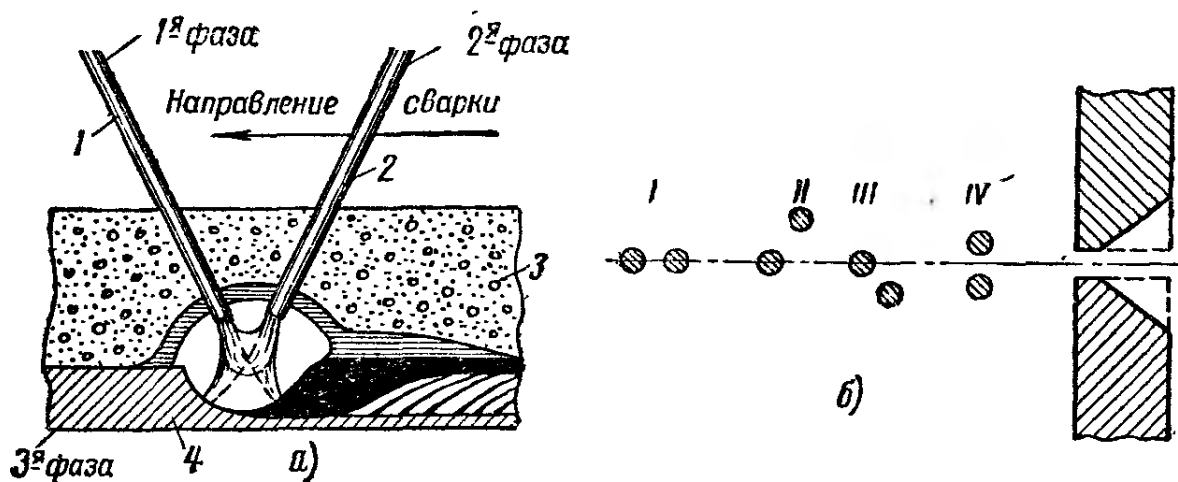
Автоматическая сварка трехфазной дугой под флюсом:
